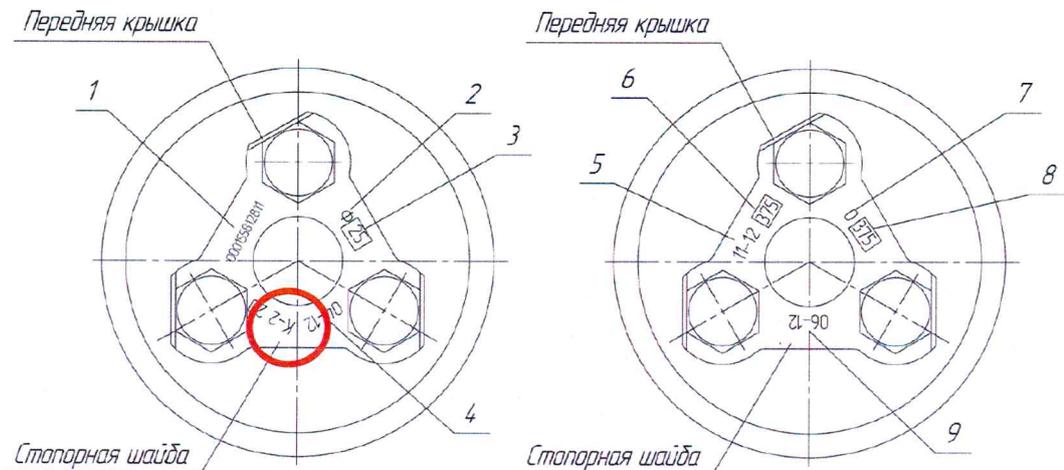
Внешний отличительный признак подшипников кассетного типа в габаритных размера 130x250x160 мм и 150x250x160 мм под адаптер для крепления тремя болтами М24
